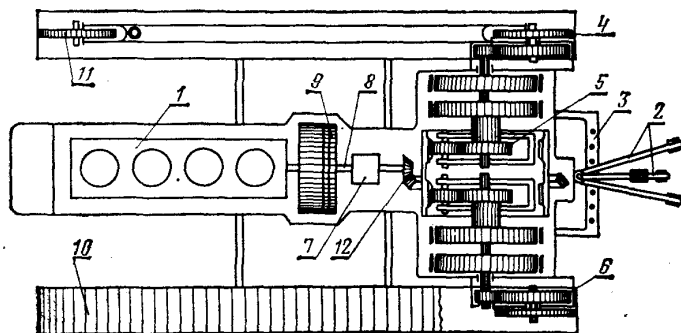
Схема розміщення основних частин, їх механізмів і деталей гусеничного трактора ДТ-75М: 1 – двигун; 2 – гідравлічна навісна система; 3 – причіпний пристрій; 4 – ведуче колесо; 5 – планетарний механізм; 6 – кінцева передача; 7 – коробка передач; 8 – з'єднуючий вал; 9 – зчеплення; 10 – гусеничний ланцюг; 11 – направляюче колесо; 12 – головна передача
